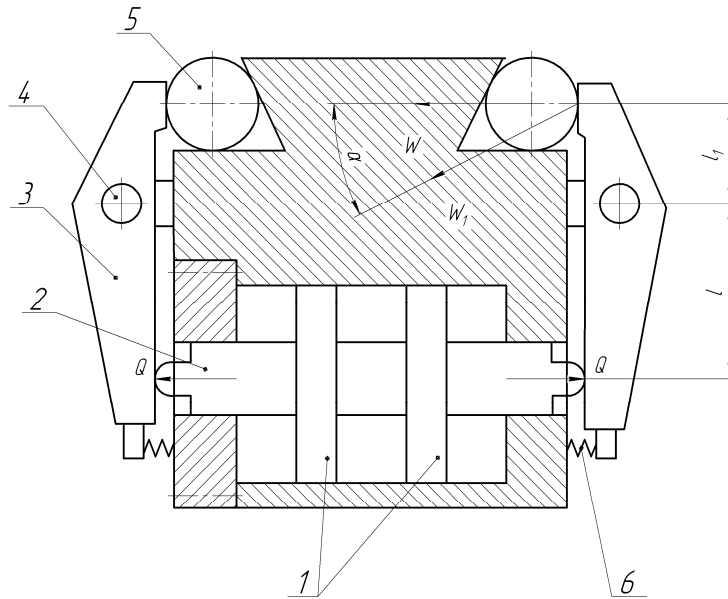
Схема й параметри комбінованого затискного пристрою із пневмоциліндром: 1 – поршень пневмоциліндра; 2 – шток пневмоциліндра; 3 – важіль; 4 – вісь важеля; 5 – деталь; 6 – пружина; W , W_1 – сили затискача деталі; Q – сила на штоку; l_1 , l_2 – довжини плечей планки; α – кут між напрямками прикладання сил затискача деталі
